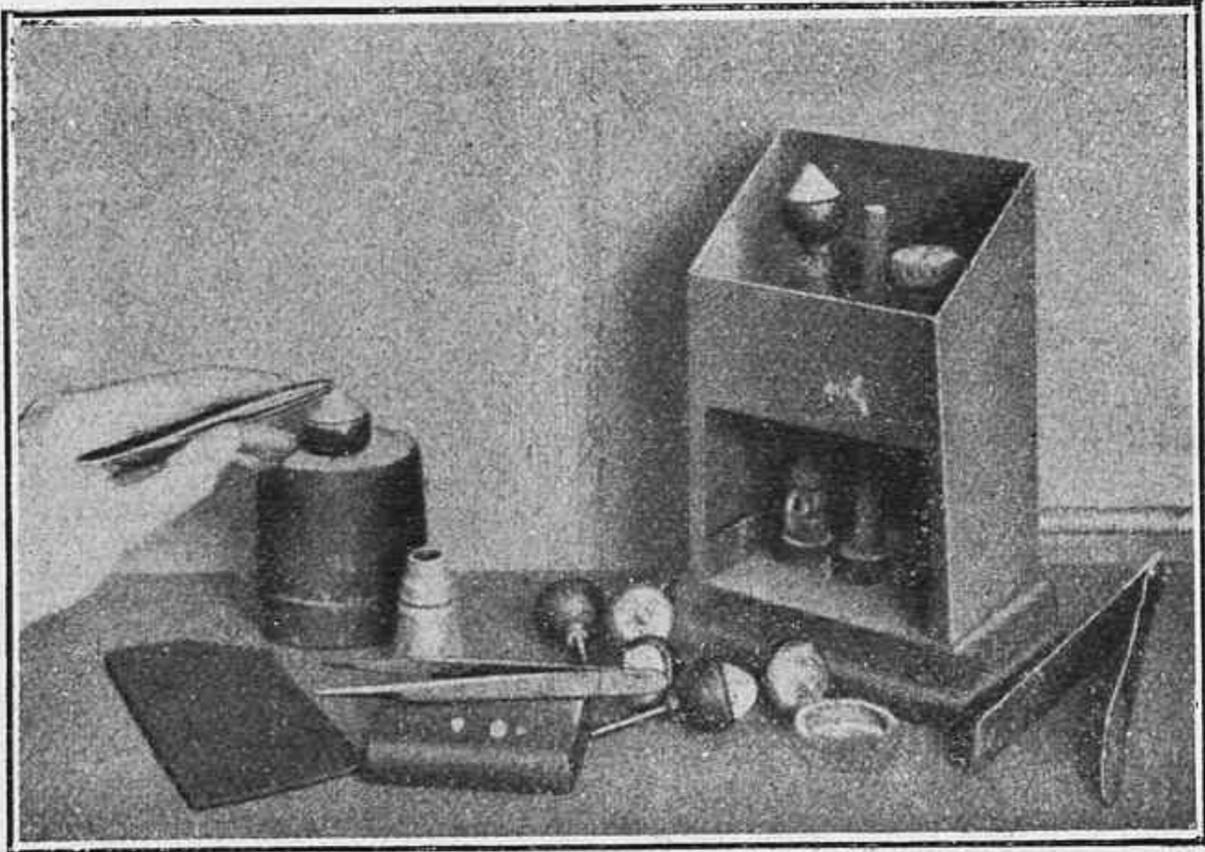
SOLDADURA DE DIAMANTES, AL SOPORTE,
